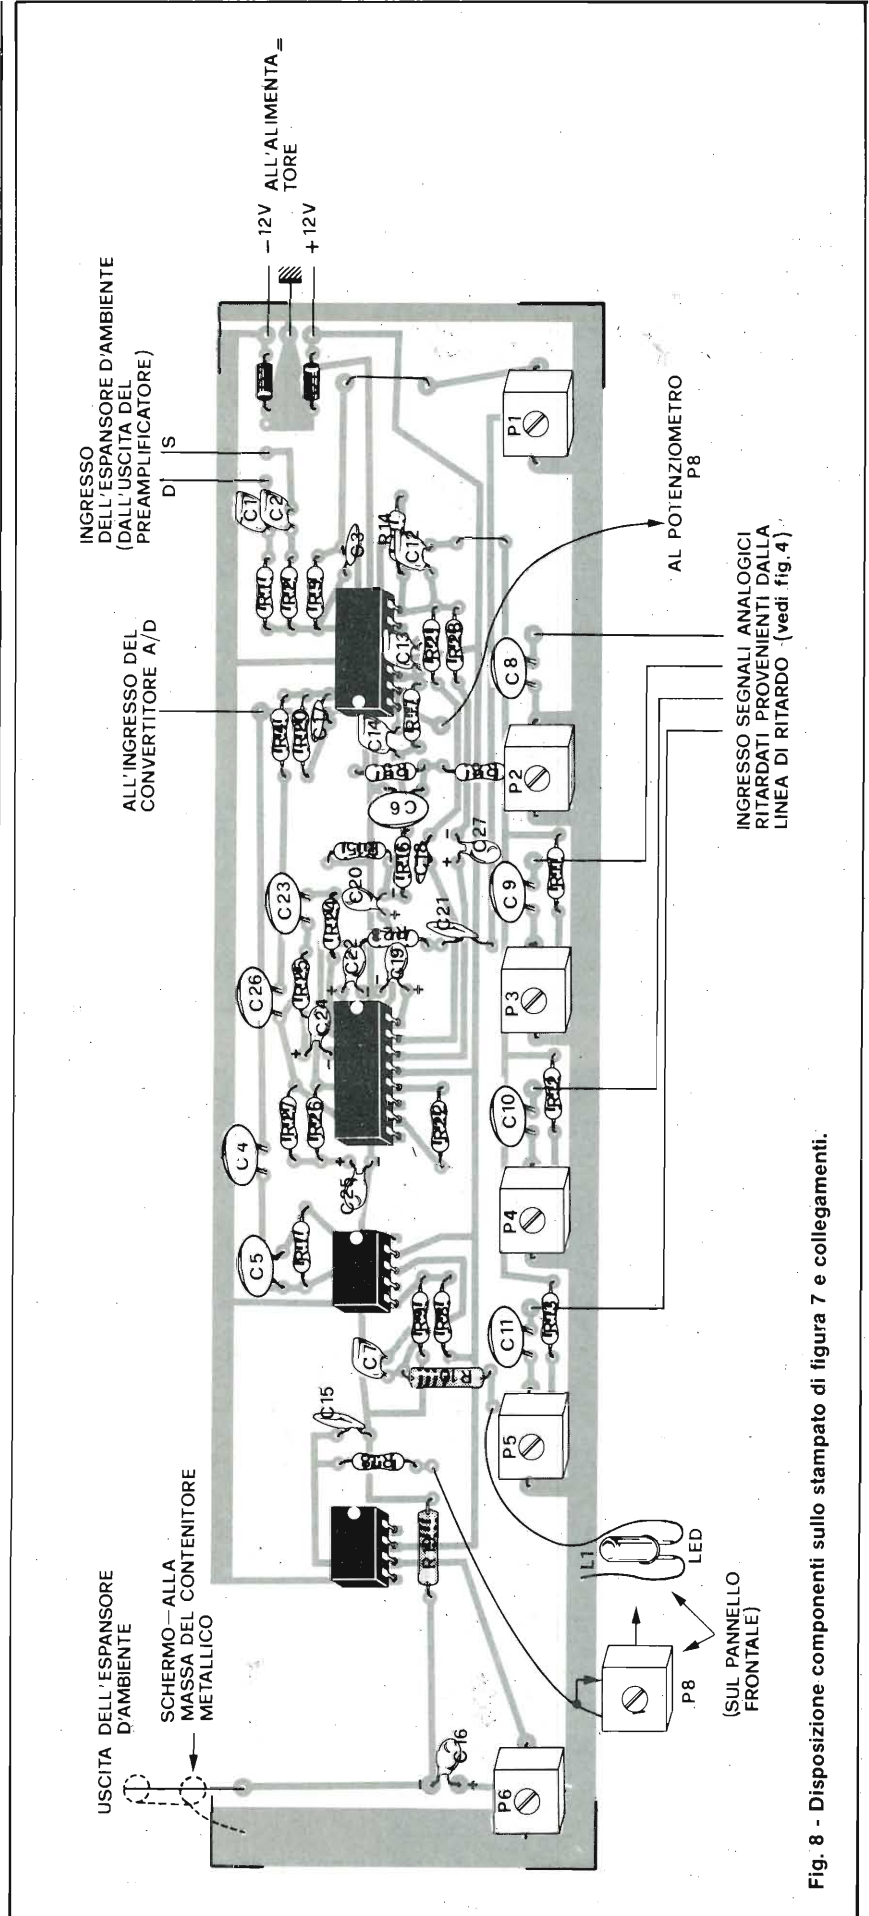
Disposizione componenti sullo stampato di figura 7 e collegamenti.
